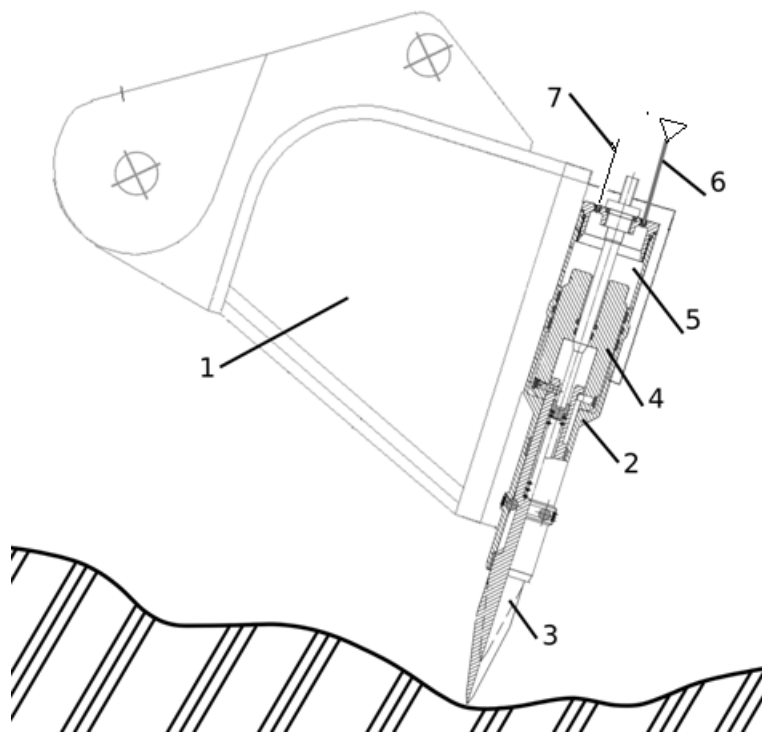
Конструктивна схема віброударного ковша: 1 – ковш, приєднаний до маніпулятора; 2 – корпус; 3 – інструмент-зубець і 4 – бойок; 5 - камера пневмоаккумулятора з початковим тиском p_0 ; 6 – лінія керованої пневмоподачі; 7 – електровиведення інформації від датчика тиску.
